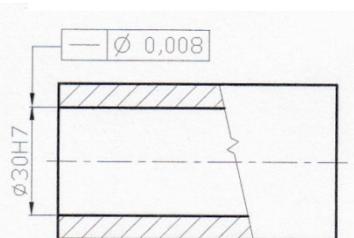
, Predpis tolerancie priamosti, tolerančné pole je ohraničené priamkami
